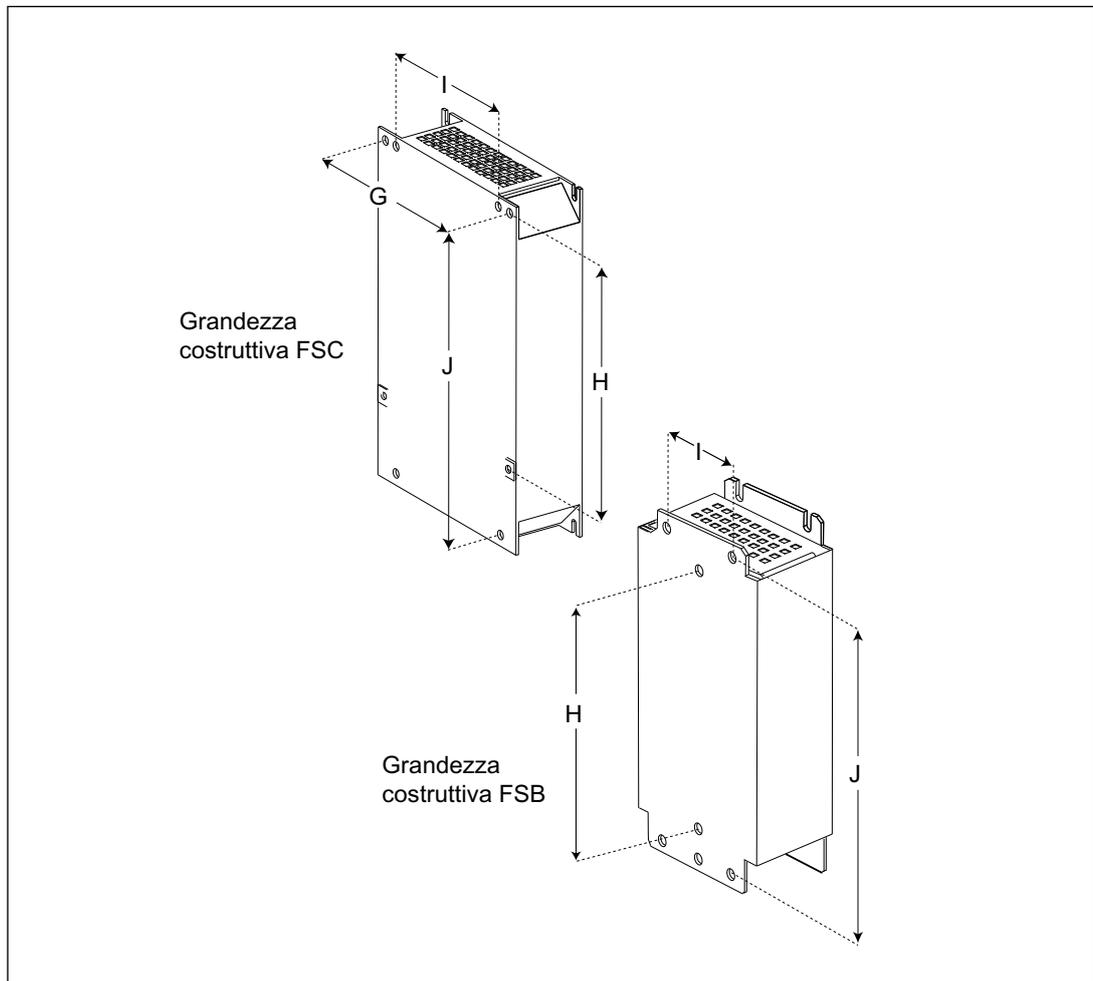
Quote di montaggio bobina motore, grandezza costruttiva FSB e FSC
